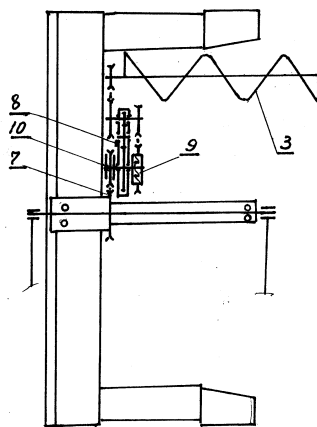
Кинематическая схема привода конвейера: 3 – винт; 7 – звездочка привода конвейера; 8 – редуктор; 9 – муфта кулачковая; 10 – муфта фрикционная.
